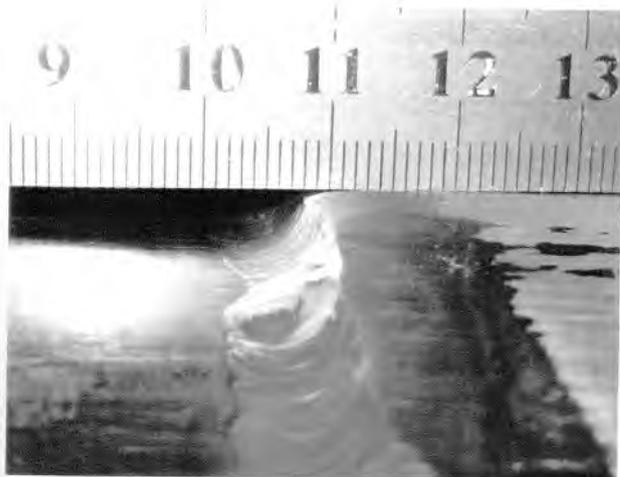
Смещение кромок в стыковом сварном соединении трубопровода. Продольные оси свариваемых деталей испытывают только линейное смещение, угловое смещение отсутствует
